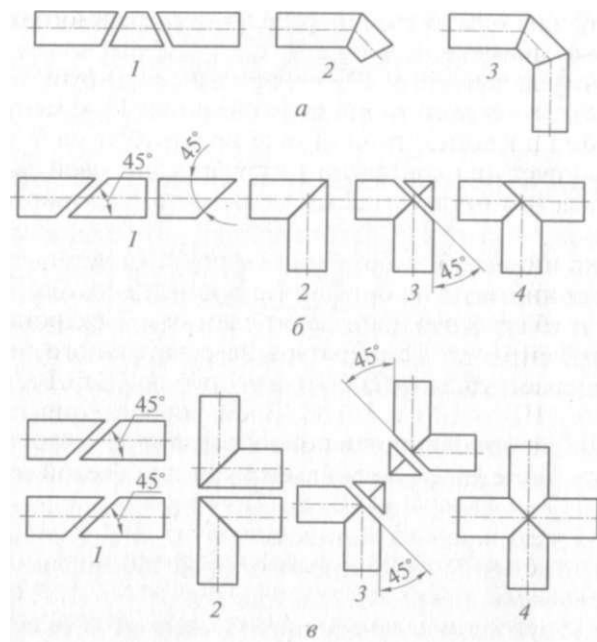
Схема изготовления сварных деталей трубопроводов: а — отводов; б — тройников; в — крестовин; 1-4 — последовательность операций (/ — резка труб, торцовка и очистка концов труб; 2 — сварка отводов; 3 — отрезка вершины отводов для тройников и крестовин; 4 — сварка)
